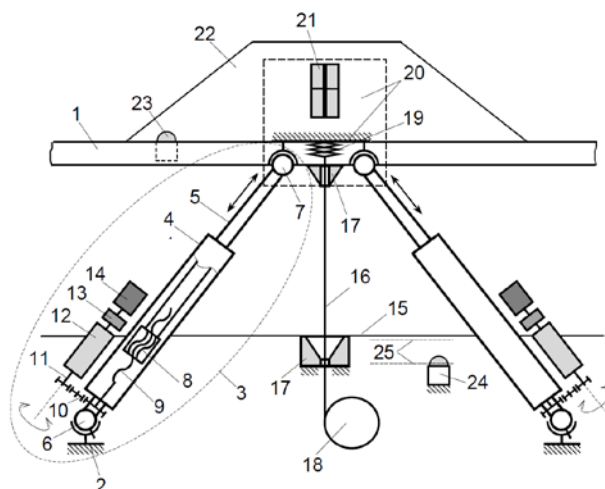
Кинематическая схема пары штанг стыковочного механизма
